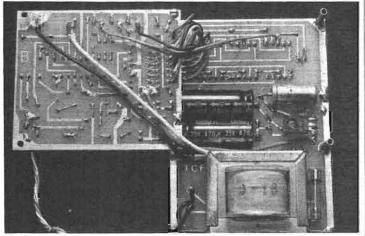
Photo E. – Disposition des deux platines pendant la pose des fils souples d'interconnexion. Noter les points de soudure des trois fils d'alimentation sur B.
